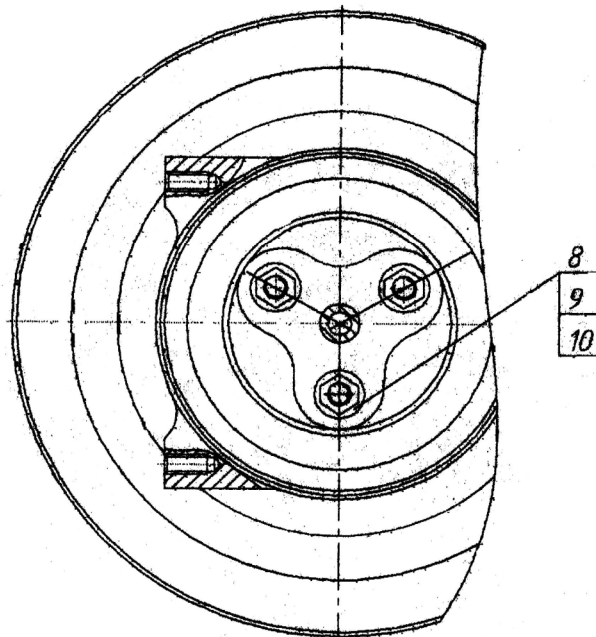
Конструктивная схема крепления узла запуска к крышке газогенератора
